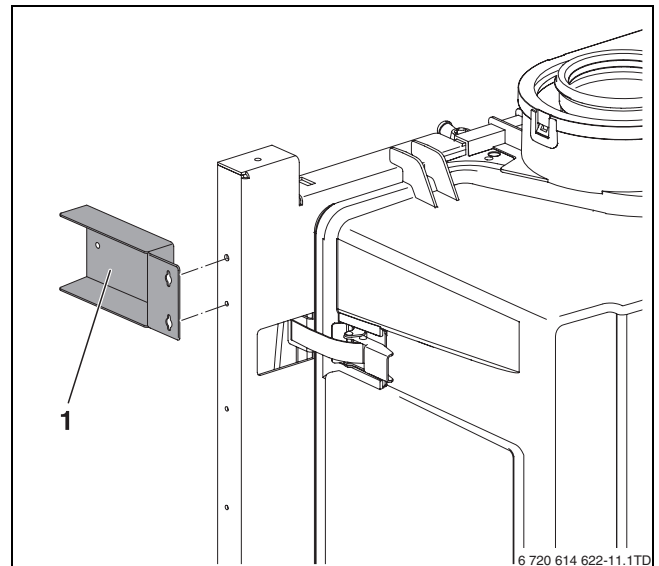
Montaggio del supporto di lamiera per il modulo solare SM10
